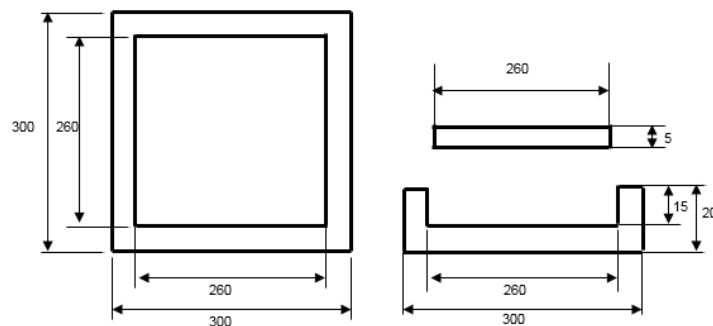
Ukuran Specimen Uji Impact Standar ASTM D 256-00
